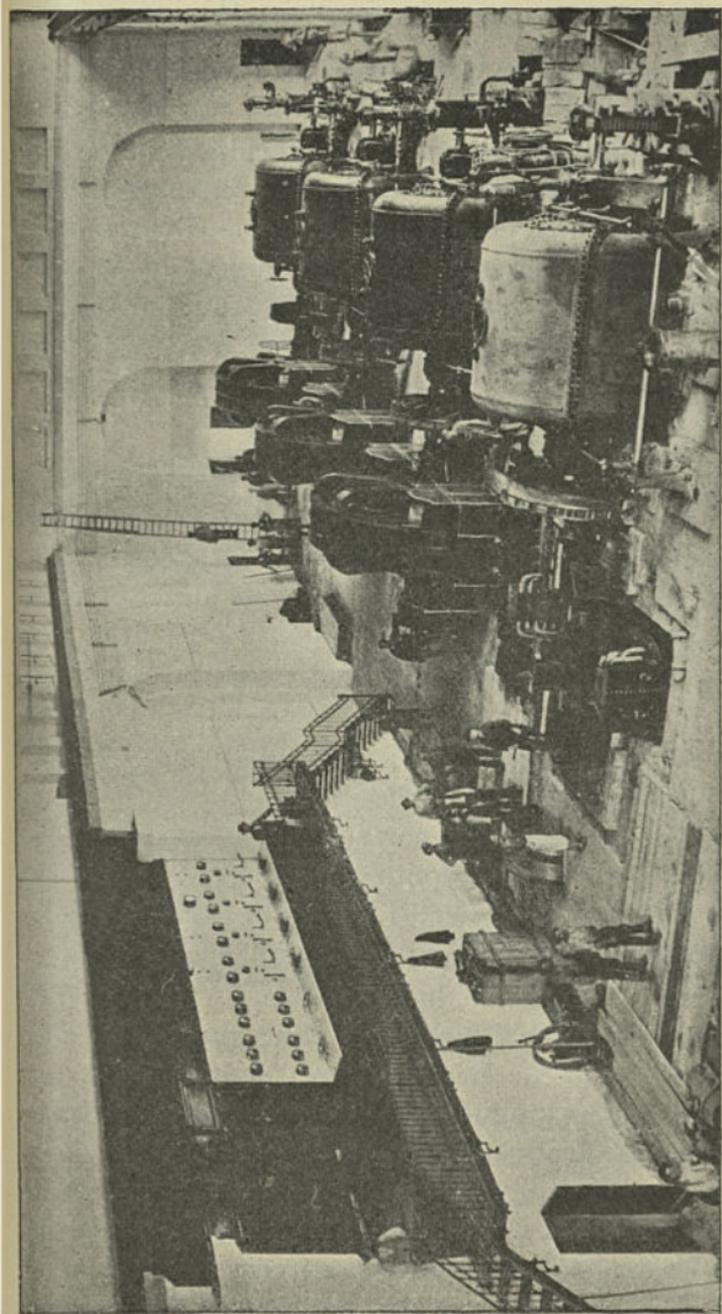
Vue intérieure de l'usine de Paderno. — Alternateurs et turbines en montage.
